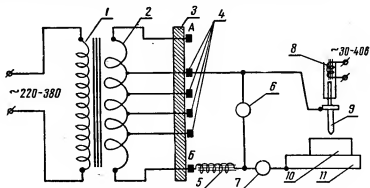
Схема использования сварочного трансформатора для восстановления посадочных мест:
